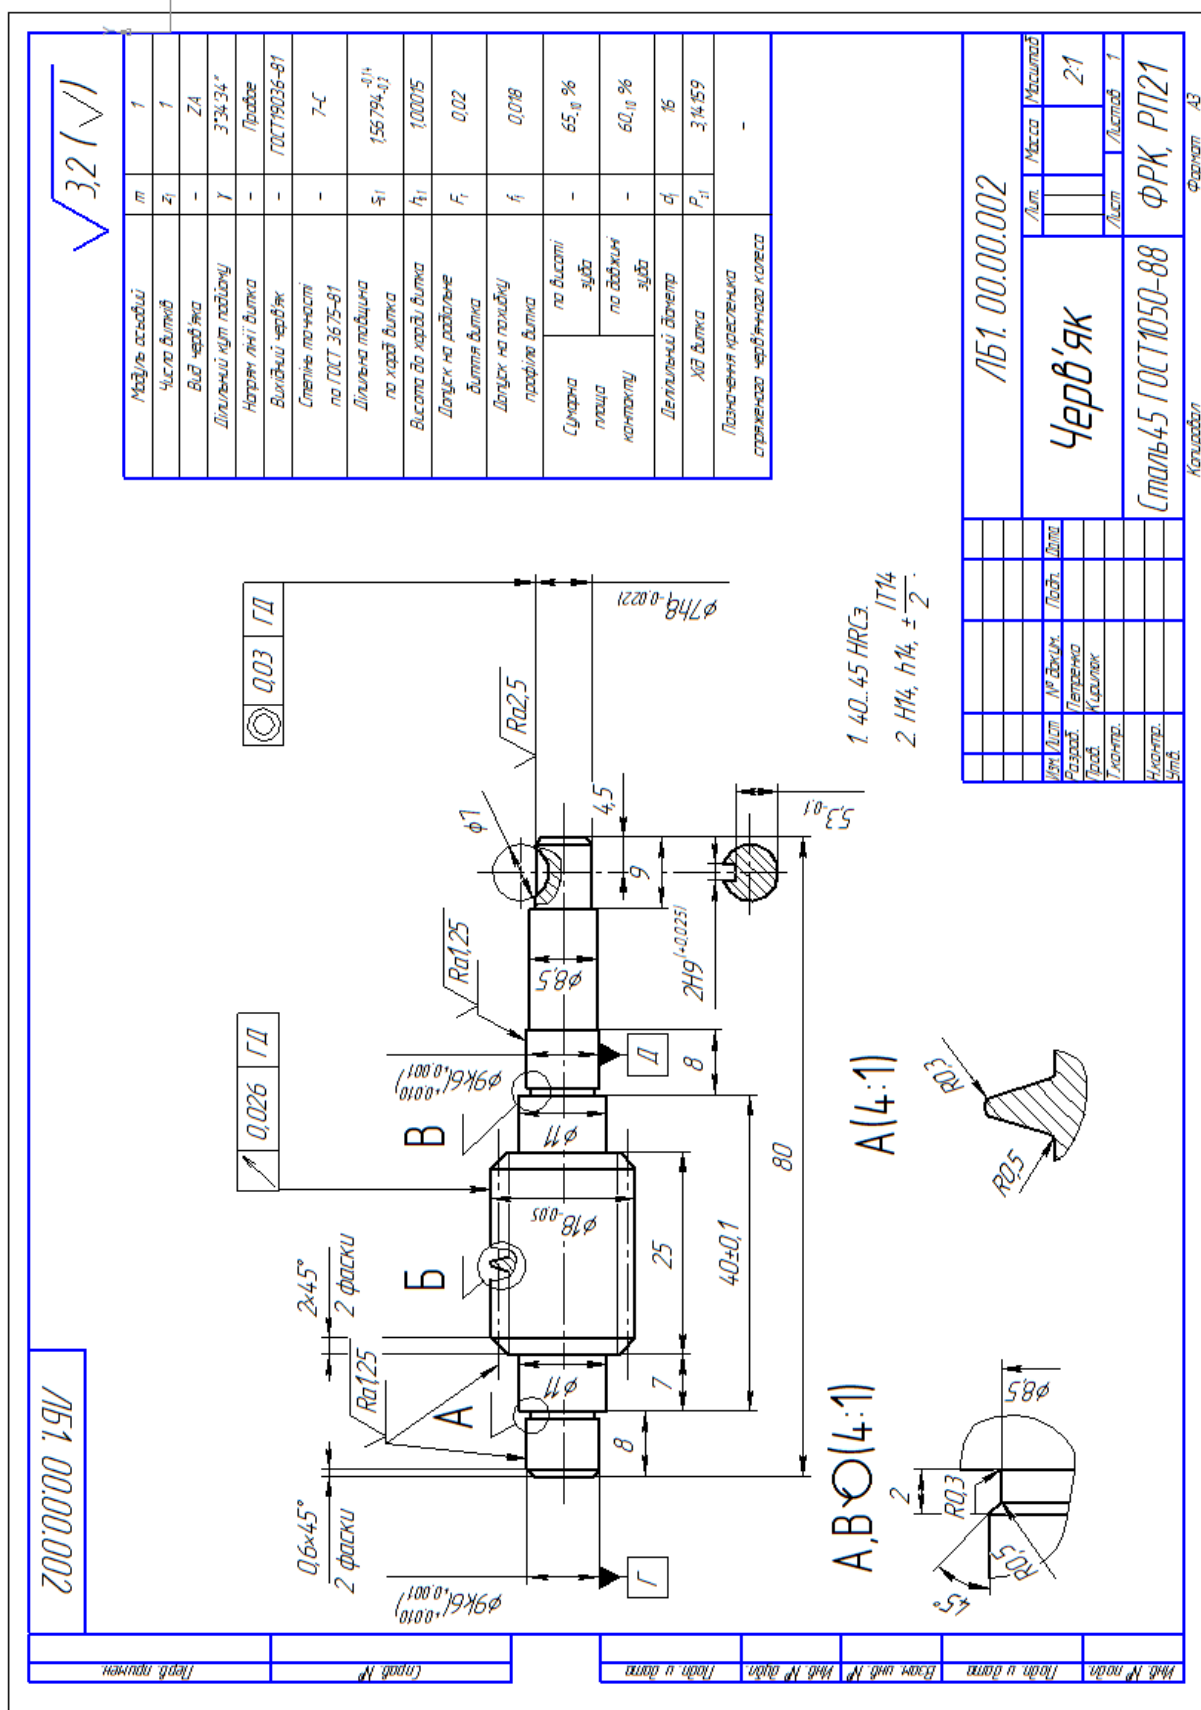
Робоче креслення циліндричного архімедового черв'яка
